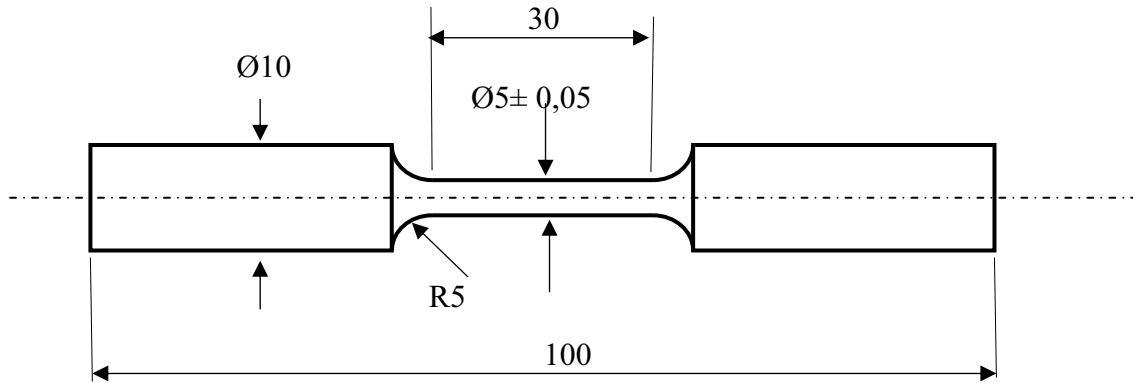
Dimensões em mm do corpo-de-prova para ensaio de tração, orientação longitudinal.
